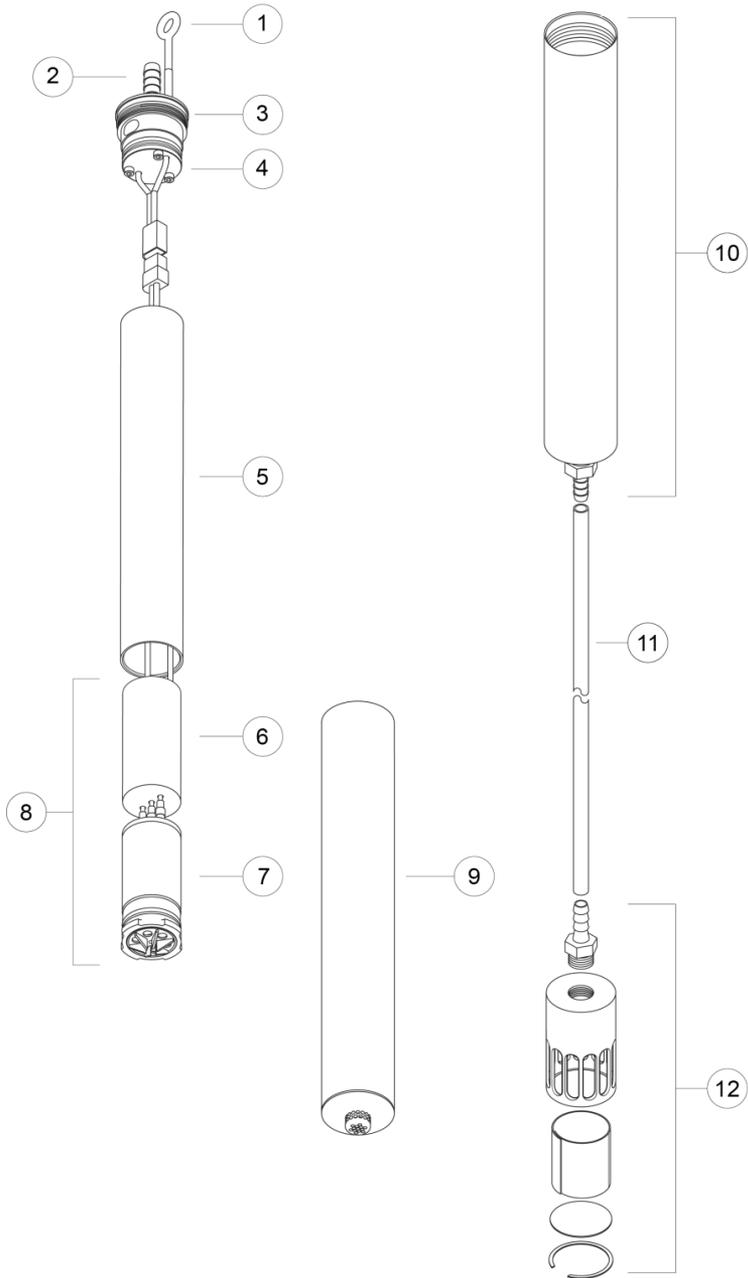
SS Geosub Pump y Drop Tube Assembly
